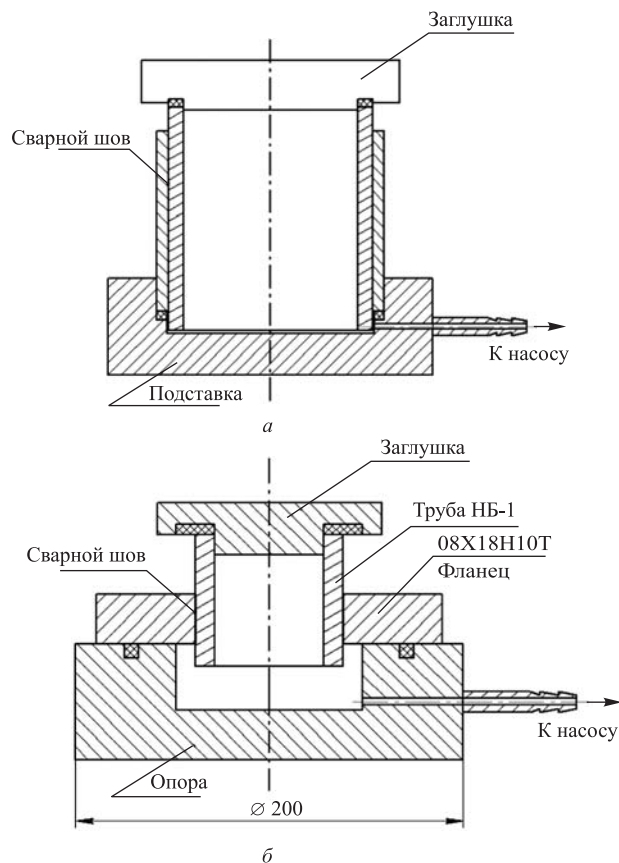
Конструкции макетов для проверки герметичности с наружной (а) и внутренней (б) плакировкой стали ниобием
